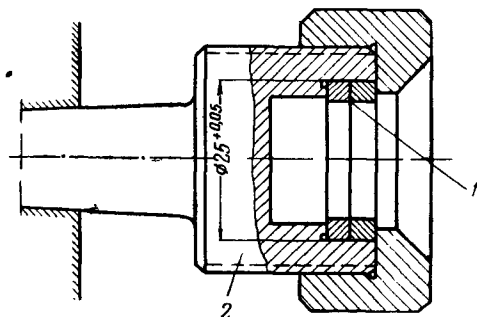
Обработка поршневых колец по внутренней поверхности:
